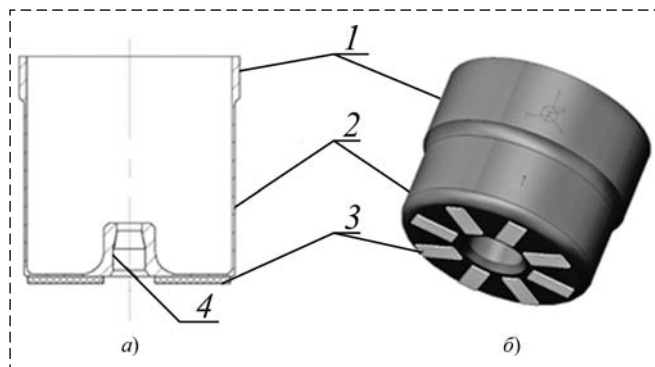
Разрез (а) и общий вид (б) цилиндрического резонатора:
